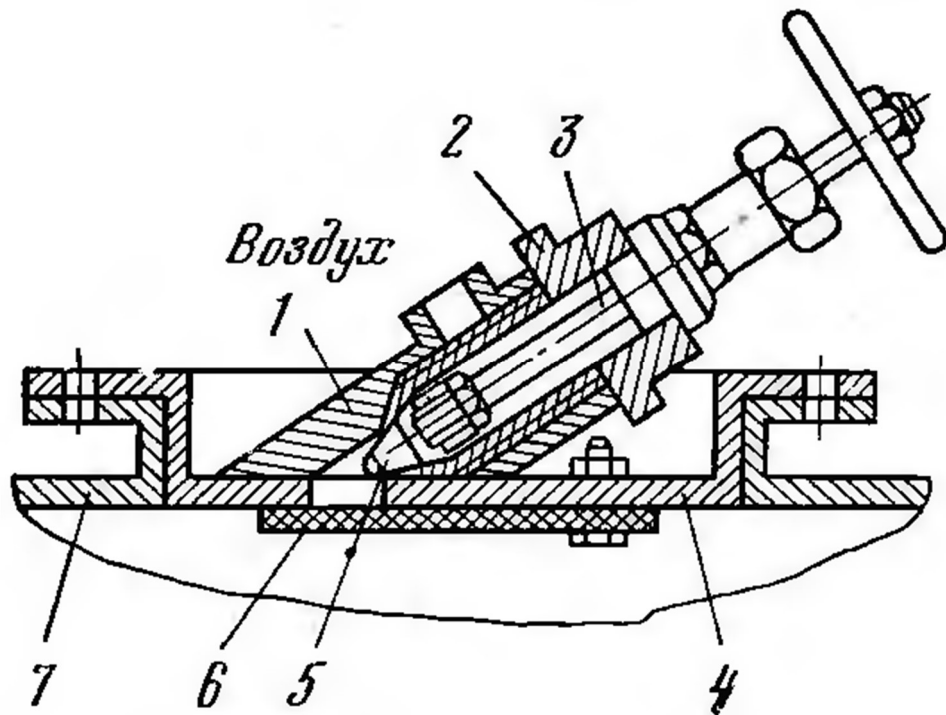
Пневмоэжектор с обратным клапаном для подачи сжатого воздуха в закладочный трубопровод: 1 – патрубок; 2 – конус эжектора; 3 – шток; 4 – стальная пластина; 5 – запорное устройство; 6 – резина; 7 – трубопровод [5]
